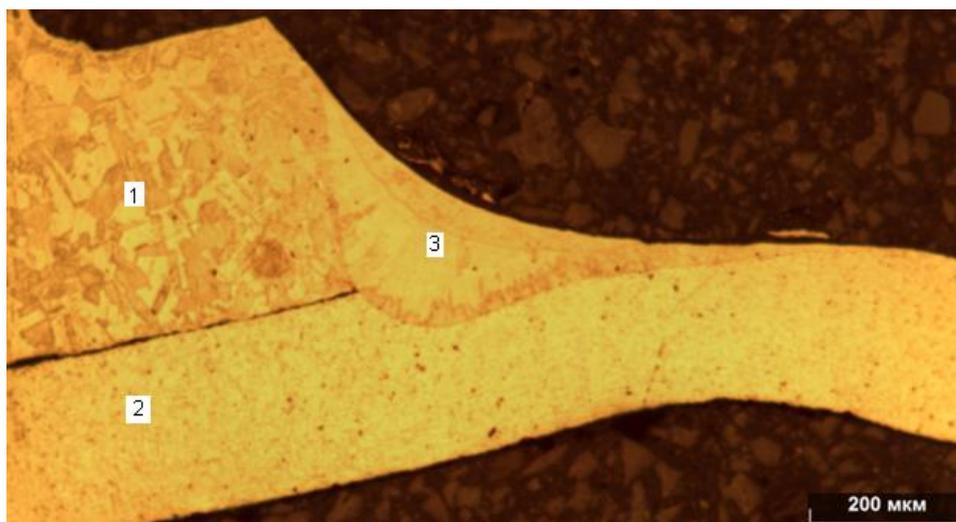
Поперечное сечение сварного шва при сварке по исходному варианту, мощность лазерного излучения при сварке 700 Вт:
